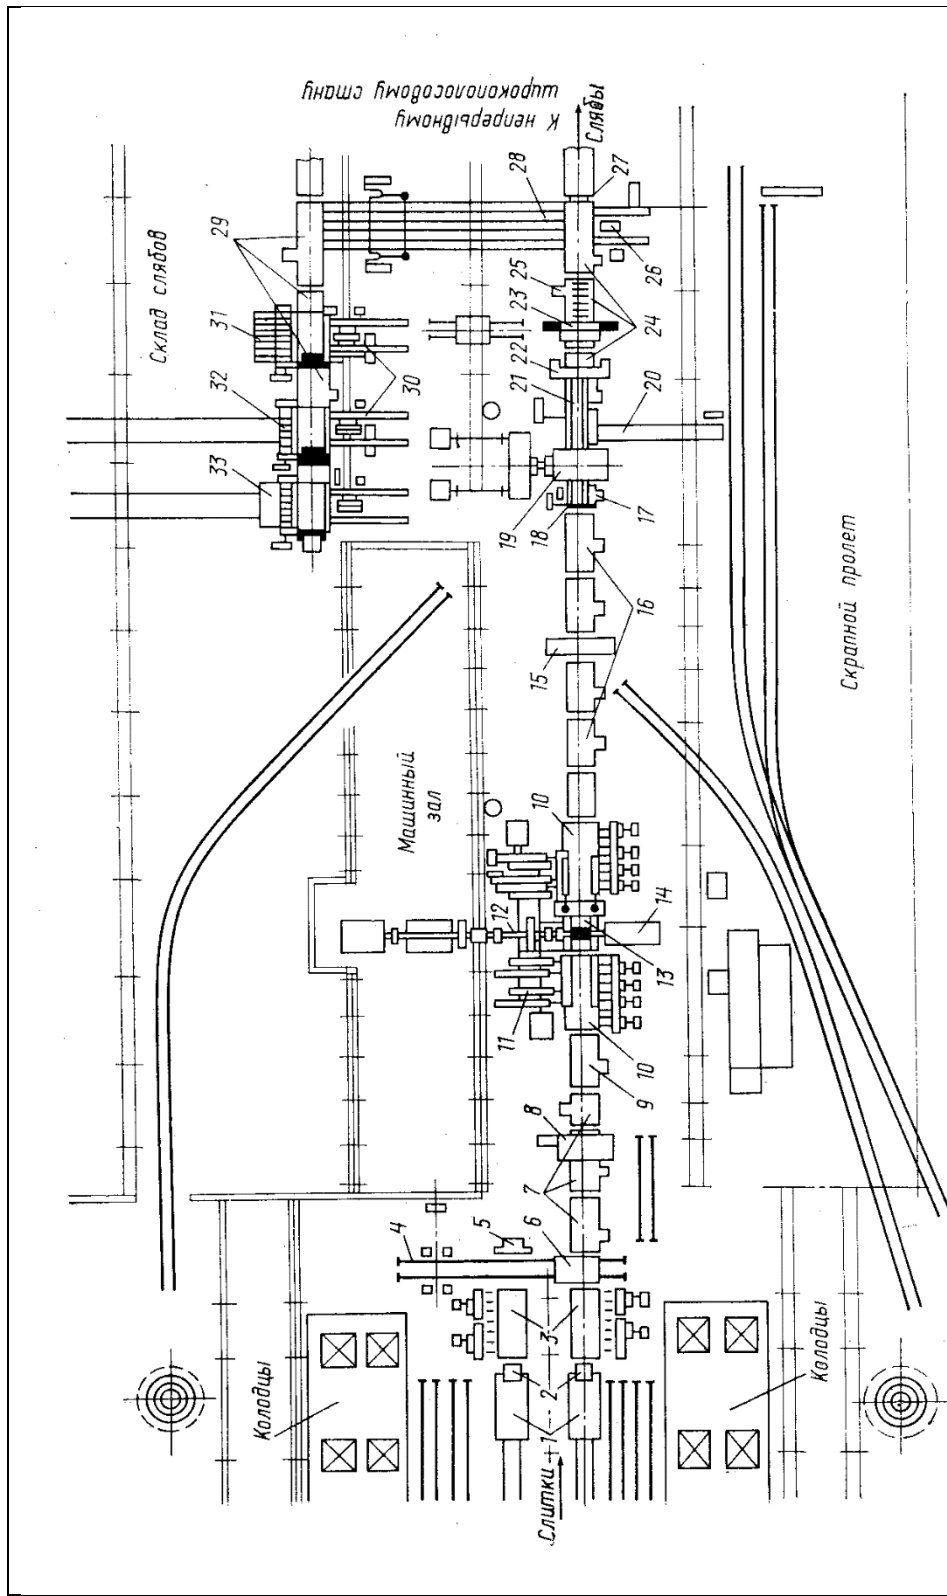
Схема расположения оборудования слябинга 1150 (1250): 1 — слитковозы; 2 — упор слитковоза; 3 — приемные рольганги; 4 — рельсовый путь; 5 — стационарный упор; 6 — рольганг-тележка; 7 — подводящие рольганги; 8 — весы с поворотным устройством; 9 — раскатной рольганг; 10 — рабочие рольганги перед и за станом; 11 — манипулятор с кантователем; 12 — универсальные шиндели; 13 — универсальная рабочая клетка с горизонтальными и вертикальными вальками; 14 — устройство для смены валков; 15 — машина огневого зачистки; 16 — транспортные рольганги; 17 — рольганг перед ножницами; 18 — сталкиватель отрезков; 19 — ножницы усиленем 20 МН; 20 — транспортер для уборки отрезков; 21 — передвигающийся рольганг за ножницами; 22 — передвижной упор для резки слябов на мерные длины; 23 — клеймитель; 24 — транспортные рольганги; 25 — весы, встроенные в рольганг; 26 — сталкиватель слябов; 27 — опускающийся упор; 28 — транспортер слябов; 29 — рольганги; 30 — сталкиватели; 31 — стеллажи; 32 — подъемный штабелирующий стол для слябов; 33 — тележка для слябов
